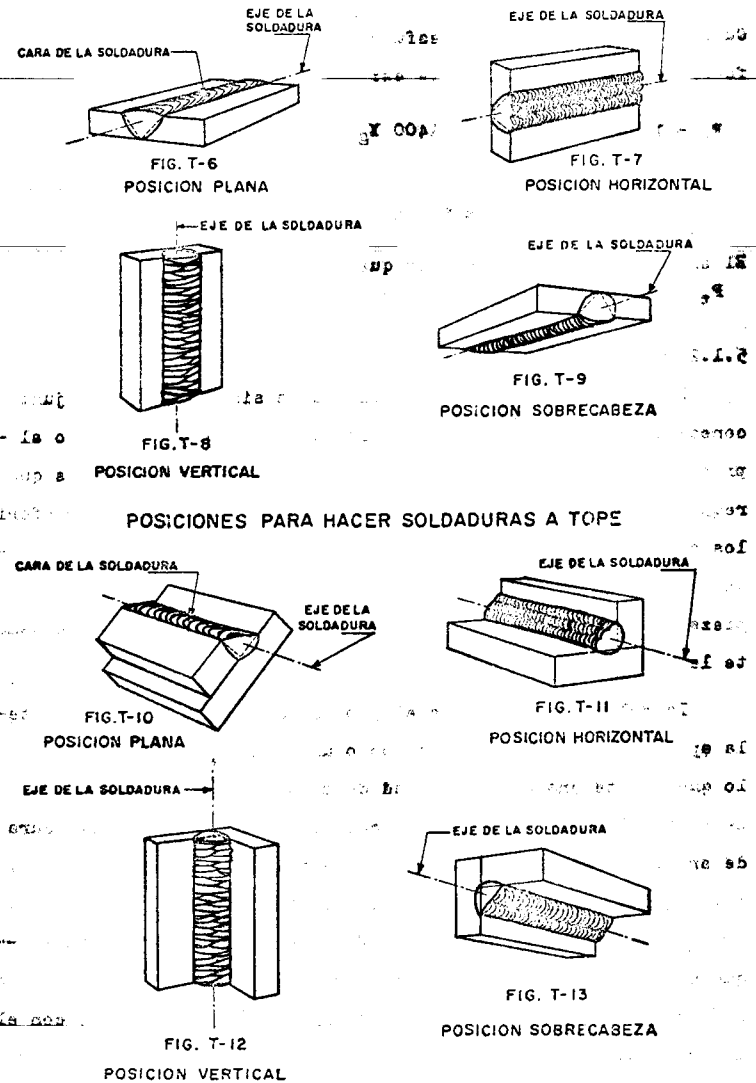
POSICIONES PARA HACER SOLDADURAS DE FILETE
